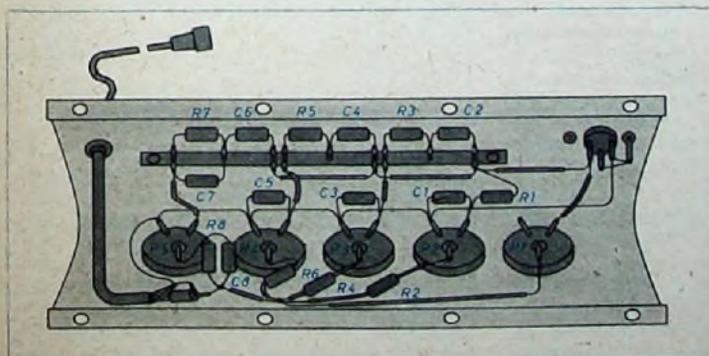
Anordnung der Verdrahtung auf der Innenseite der Aluminiumblechhaube
